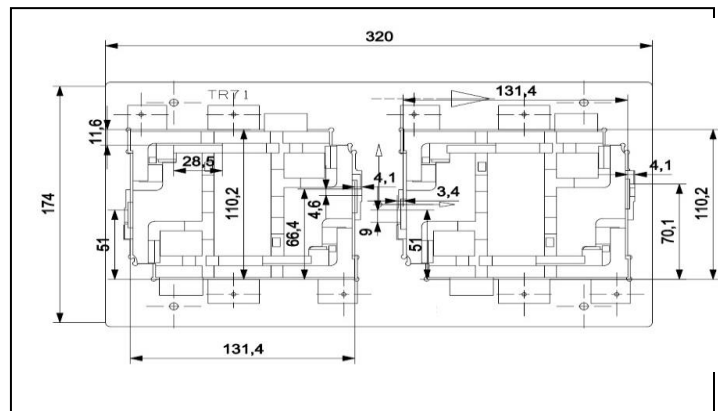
Diseño mecánico del pallet en 2D con medidas en mm.
